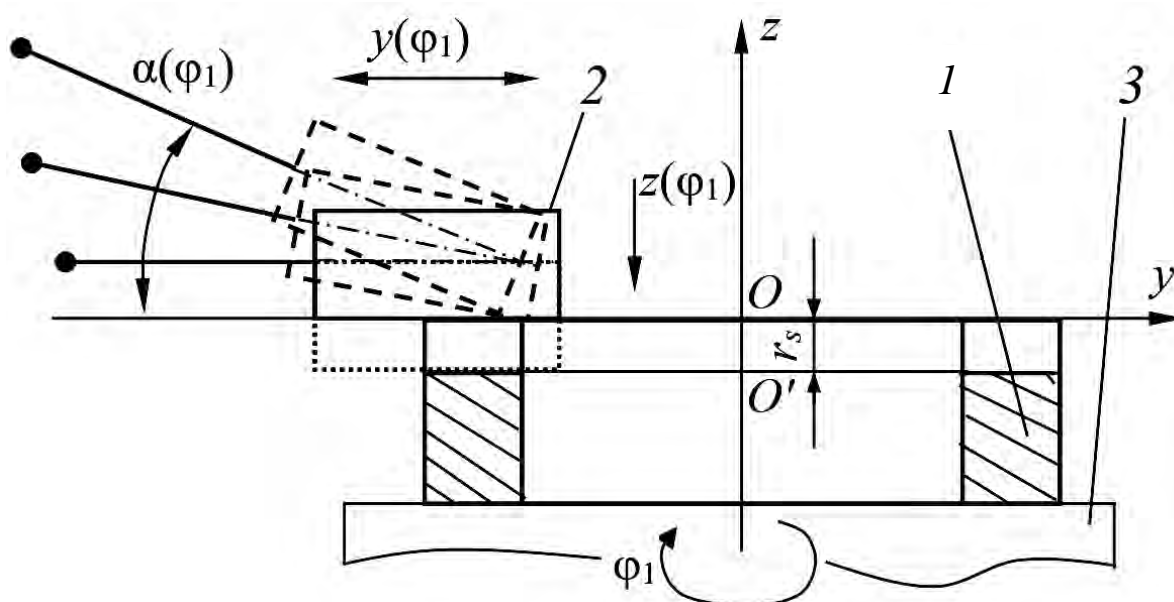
Схема согласования движений инструмента и заготовки при изготовлении кулачкового профиля: 1 – заготовка; 2 – фреза; 3 – стол
